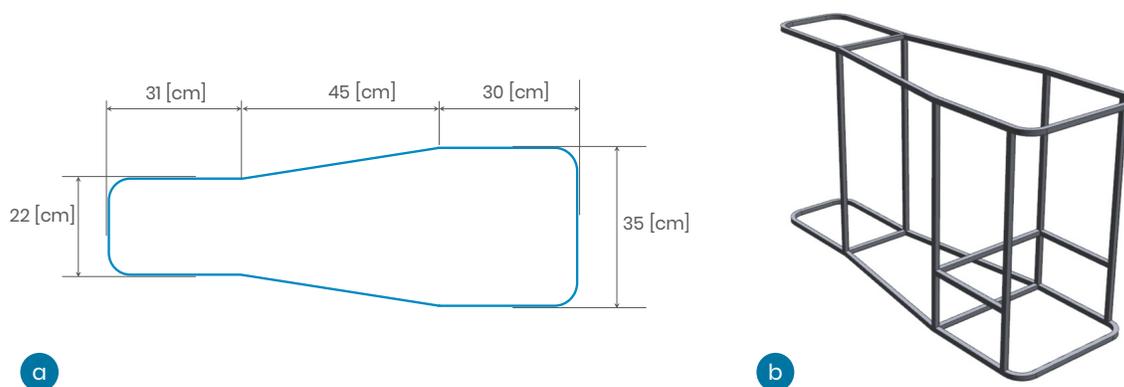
62 - a) Dimensiones planteadas VUMi3; b) Estructura preliminar VUMi3.
